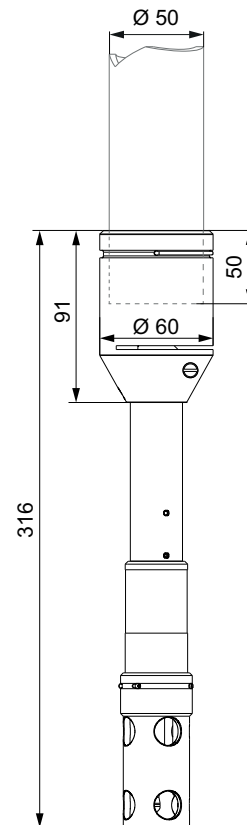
Abmessungen (in mm) des Sensorhalters; Rohr mit Außendurchmesser 50 mm nicht inbegriffen
